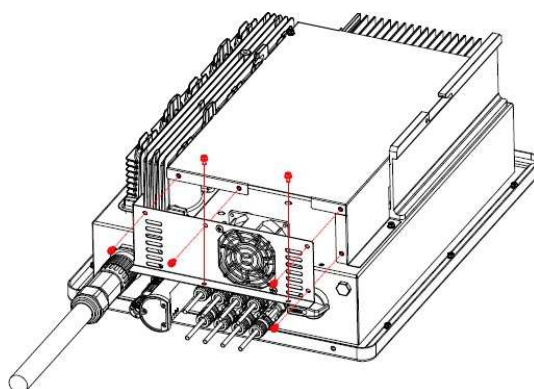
Remova os parafusos de fixação do suporte do ventilador
